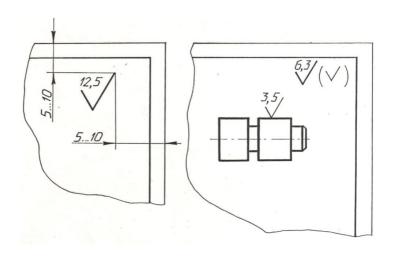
Обозначение шероховатости поверхностей деталей
